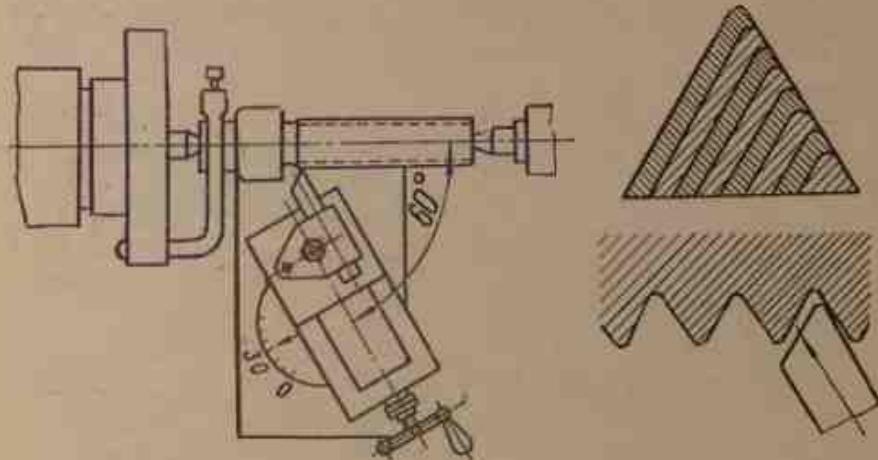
Схема работы резьбового резца при повернутых верхних салазках суппорта
